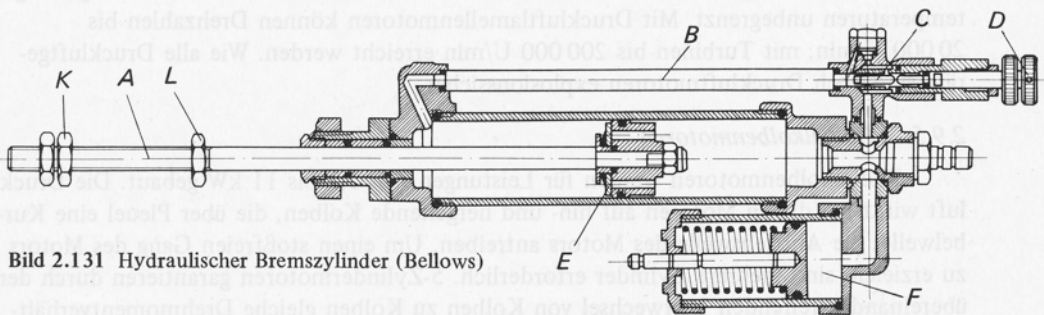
Hydraulischer Bremszylinder (Bellows)
